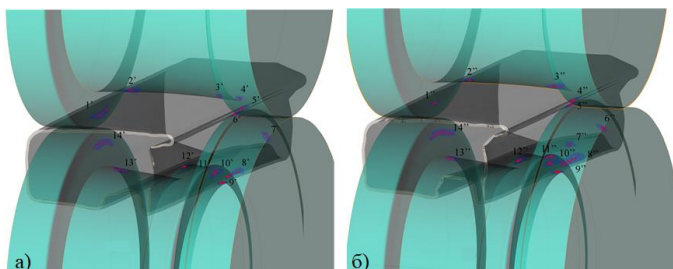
Зоны контакта инструмента и заготовки в клетке №15: а)  $\varnothing 119$  мм; б)  $\varnothing 122$  мм
